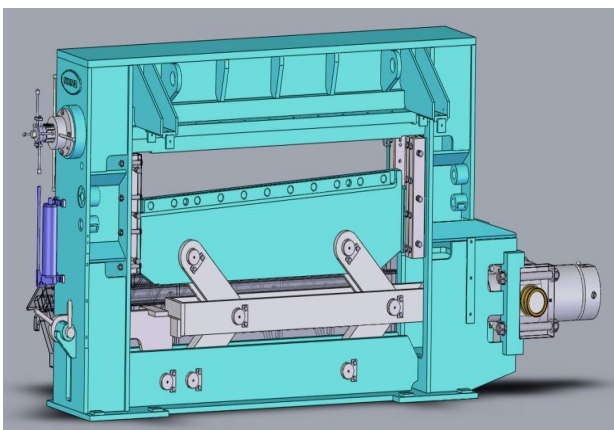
Конструкція ножиць для поперечного розрізання плоского металопрокату з нижнім рухомим похилим ножом («НКМЗ», м. Краматорськ, Україна)
